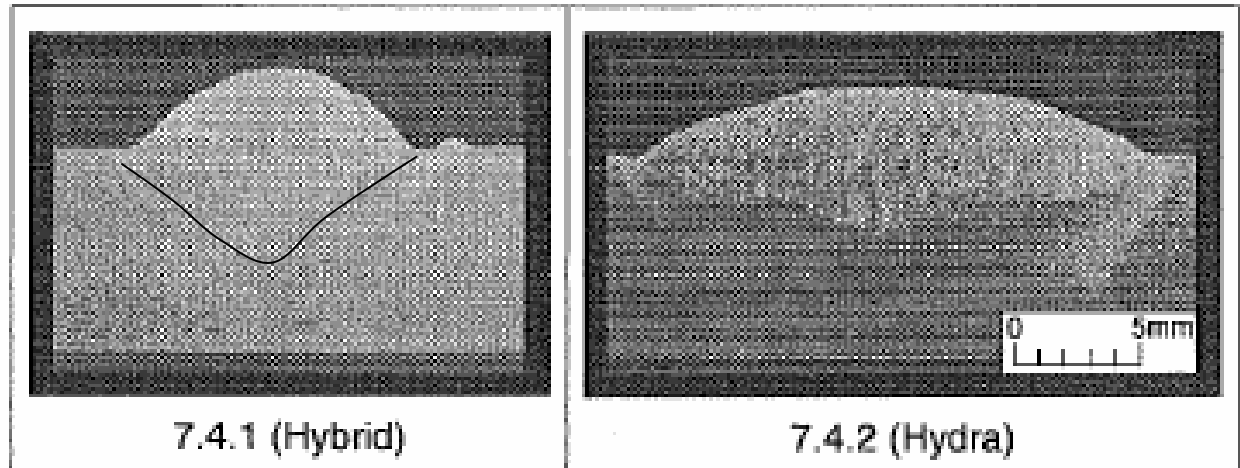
Einschweißtiefe beim Hybrid- und Hydraschweißen ($d_0 = 1,2$ mm)
